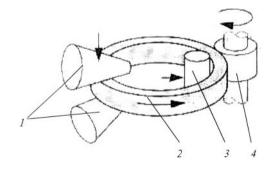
Радиально-осевая кольцераскатка: I — осевые валки; 2 — кольцо; 3 — дорновой валок; 4 — главный валок
